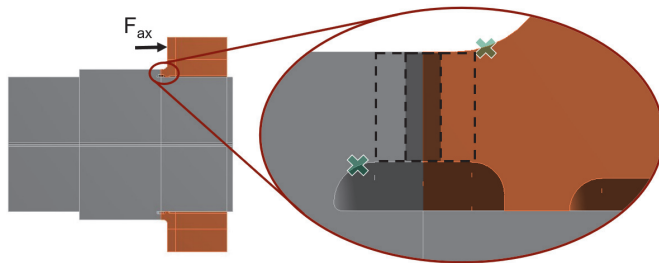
Druckkamm und Ritzelwelle im Schnitt (links) und Kerbgeometrie im Bereich der Schweißnaht (rechts), geometrische Kerben gekennzeichnet
